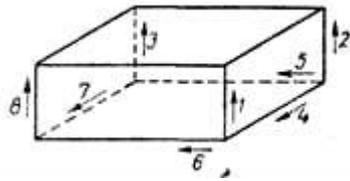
Порядок сварки коробчатого изделия
